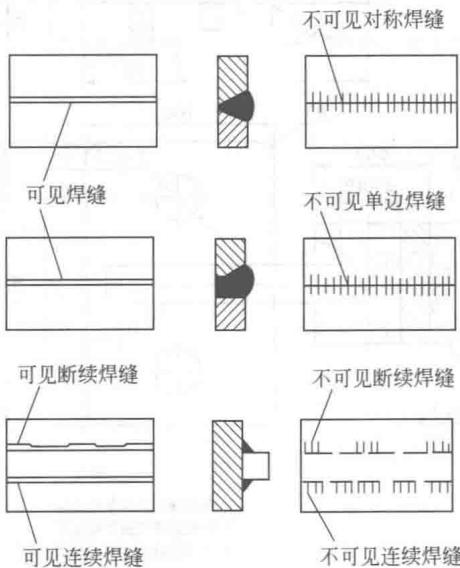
用粗实线和栅线表示焊缝的画法
